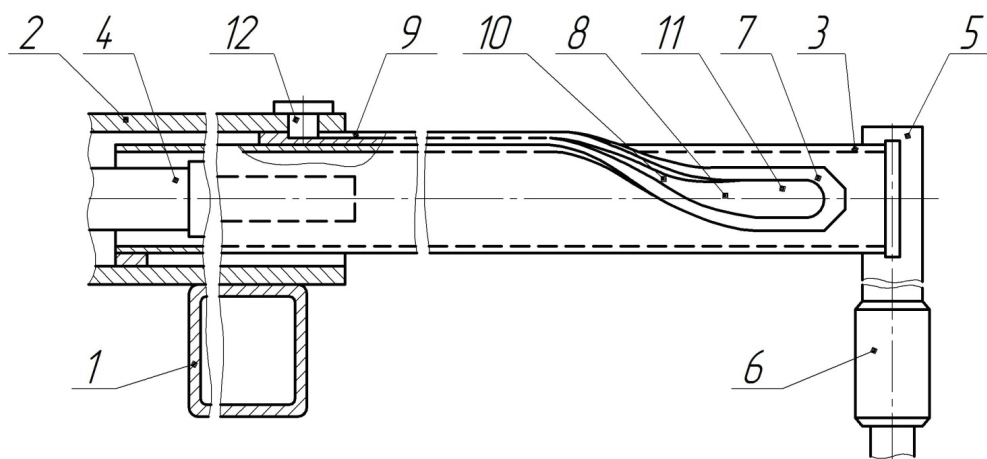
Выдвижная опора с механизмом поворота короткоходового гидродомкрата: 1 – рама; 2 – направляющая; 3 – выдвижная балка; 4 – гидроцилиндр; 5 – кронштейн; 6 – опорный гидродомкрат; 7 – направляющая дорожка; 8 – канавка; 9 – продольная проточка; 10 – винтовая проточка; 11 – продольная проточка; 12 – фиксатор.
